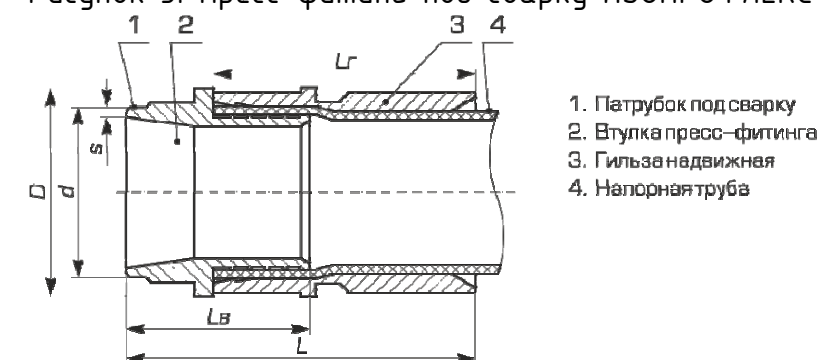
Пресс-фитинг под сварку ИЗОПРОФЛЕКС-А
